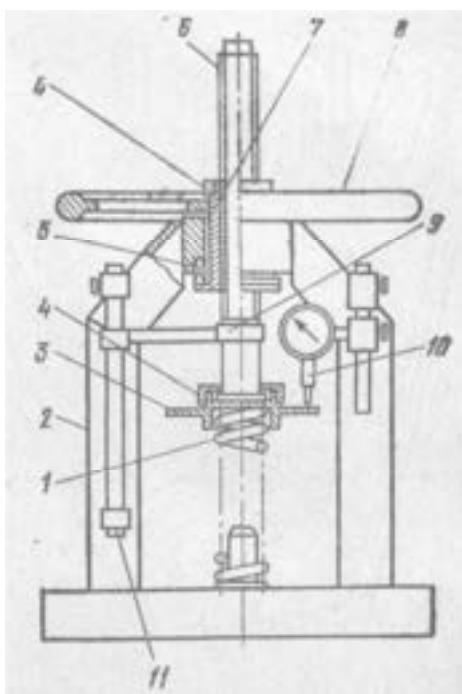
Приспособление для испытания пружин предохранительных клапанов:
